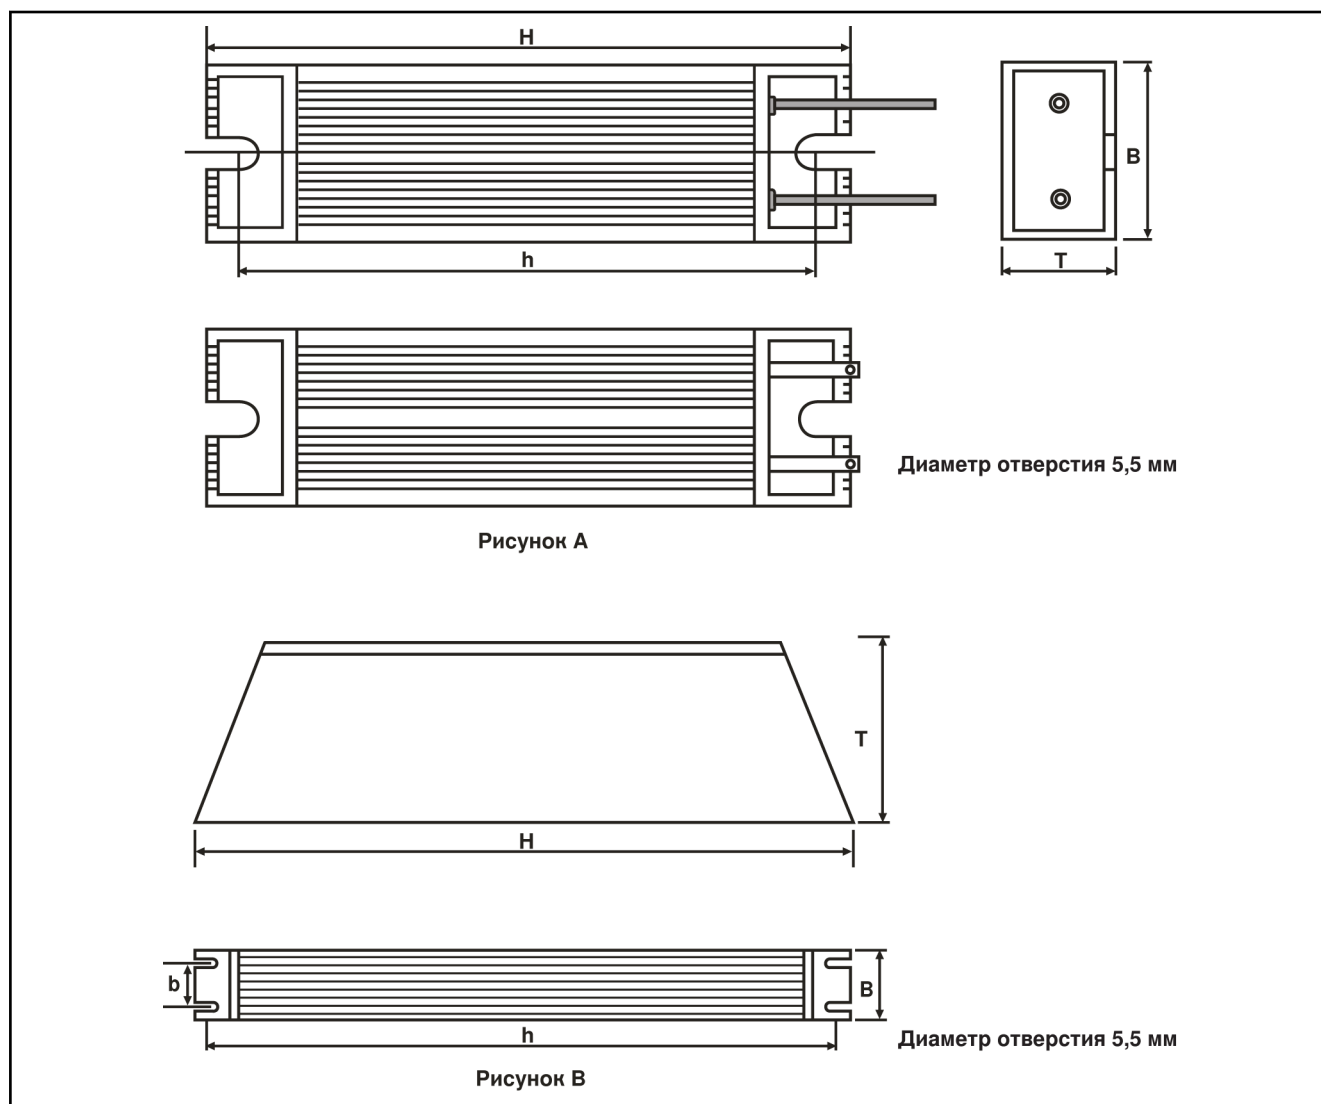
Тормозной резистор в алюминиевом корпусе
